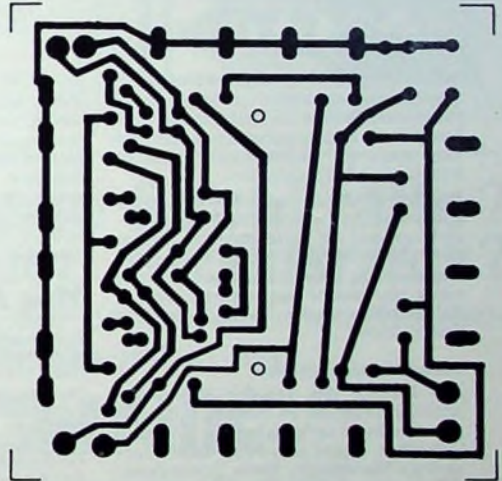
Printplatte für das Quadro-Stereo-Anschlußgerät (Maßstab 1:1)
